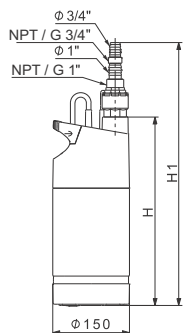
Pompă SB. aceleași dimensiuni cu sorb integrat și cu sorb cu flotor
